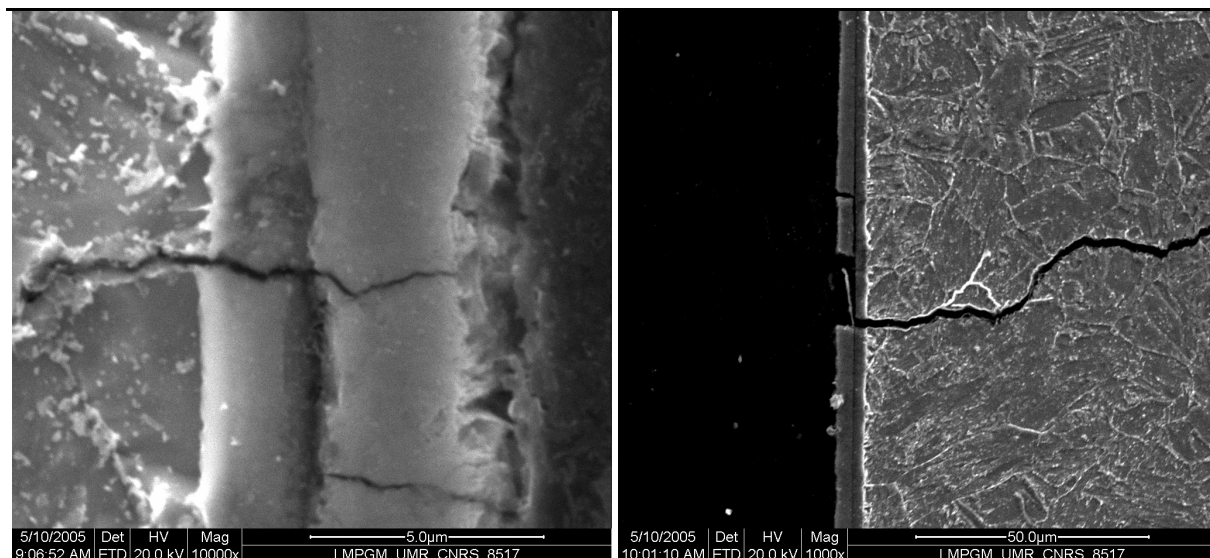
Détail d'une fissuration secondaire observée sur une coupe longitudinale d'un échantillon pré-oxydé testé en LCF ($\varepsilon_f=0,38\%$) (A_{ox})
